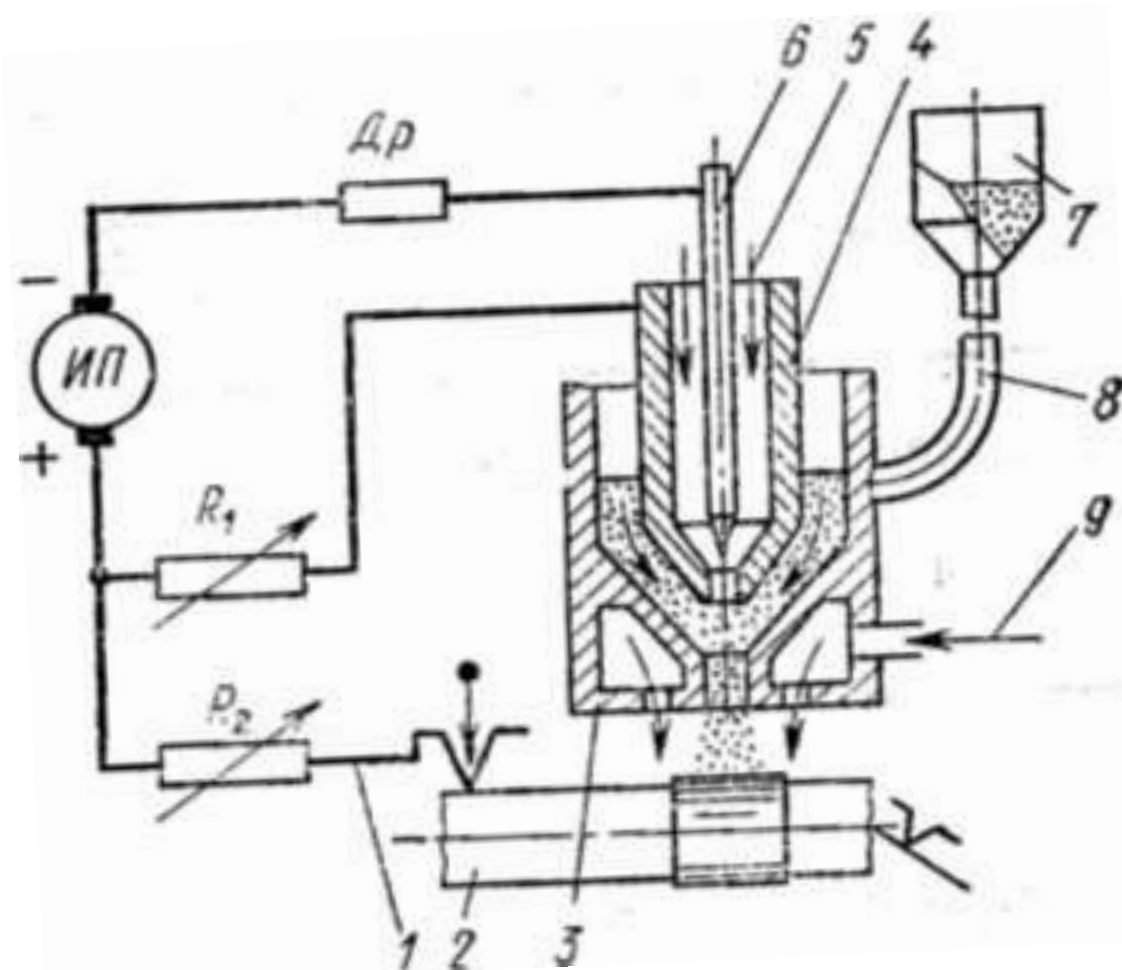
Восстановление изношенных валов наплавкой: 1 – станок; 2 – восстанавливаемый вал; 3 – наружное сопло плазмотрона; 4 – медное сопло; 5 – плазмообразующий газ; 6 – вольфрамовый катод; 7 – питатель для подачи порошка; 8 – транспортирующий газ; 9 – защитный газ; ИП – источник электрического питания; R1 и R2 – реостаты; Др – дроссель.
